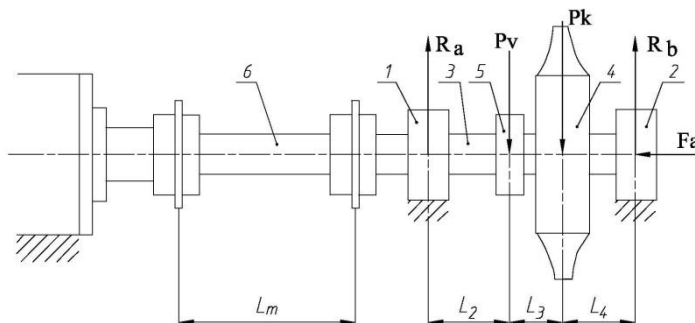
Компоновка ротора осевого вентилятора и действующие на него нагрузки: 1 – радиальная подшипниковая опора; 2 – радиально-упорная подшипниковая опора; 3 – коренной вал ротора; 4 – рабочее колесо; 5 – исполнительный механизм поворота лопаток рабочего колеса; 6 – трансмиссионный вал. P_v – нагрузка от веса исполнительного механизма поворота лопаток рабочего колеса; P_k – нагрузка от веса рабочего колеса; R_a, R_b – реакции опор; F_a – осевая нагрузка на радиально-упорную
